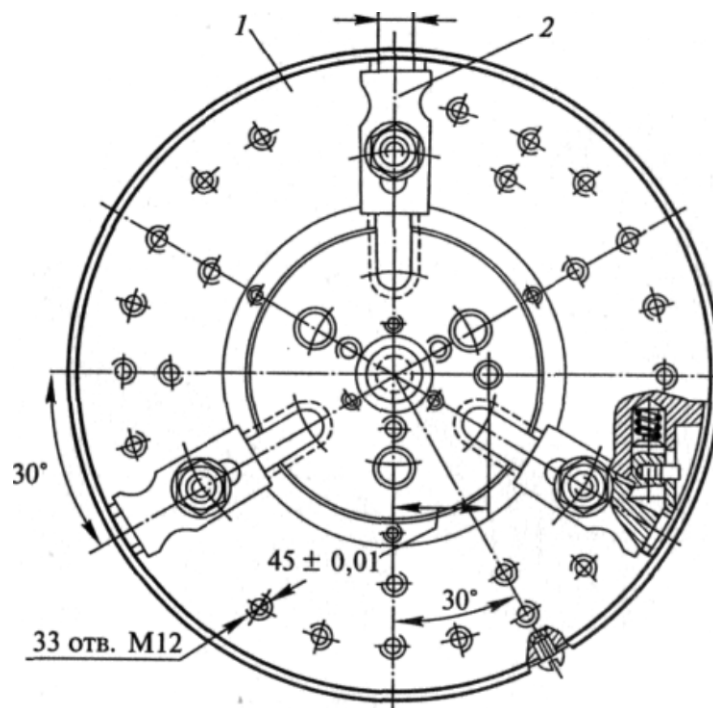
Токарна планшайба: 1 – додатковий диск; 2 – прихват
